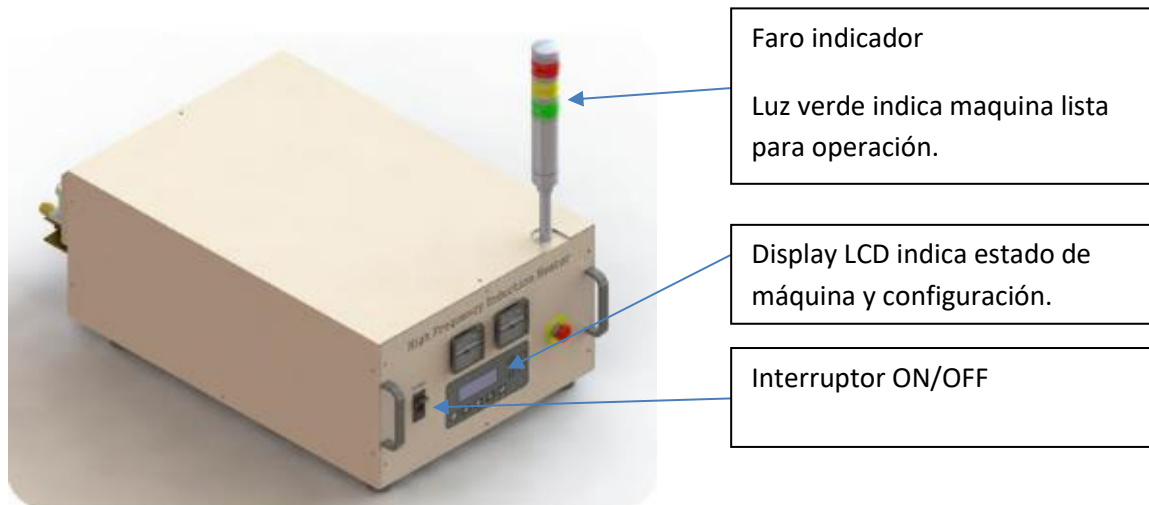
Generador para máquina soldadora de alta frecuencia. Fuente: OSUNG HITEC
